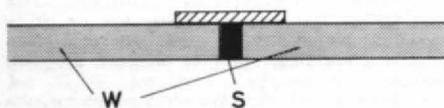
Beim Zusammenkleben der Wandteile W ein gerades Unterlegstück (schraffiert) mit ankleben, den Sägepalt S mit Stabilit ausfüllen und planschleifen!
